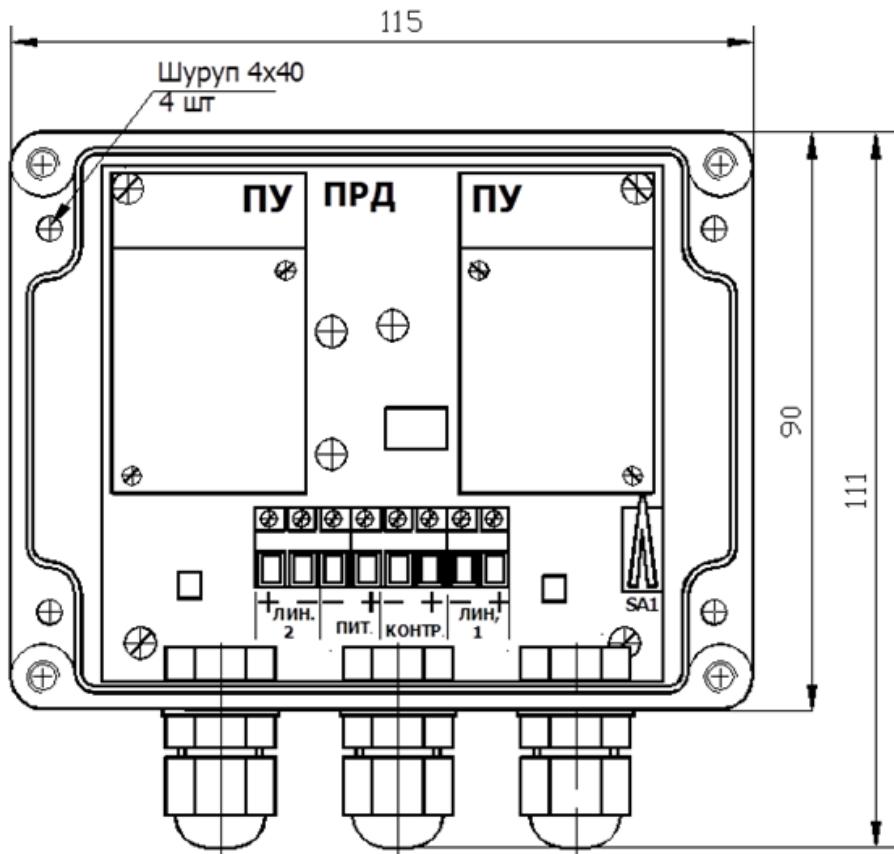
Общий вид ПРД в корпусе со снятой крышкой
